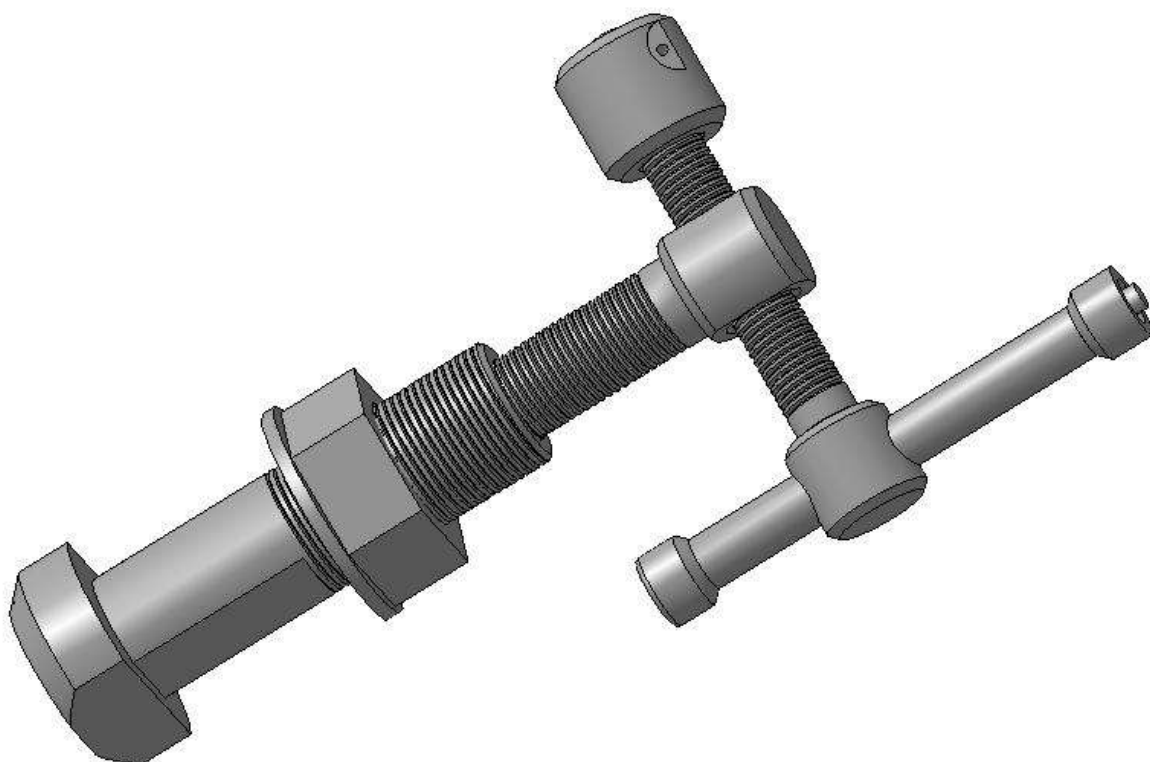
Прижим боковой, 3D сборка – общий вид
